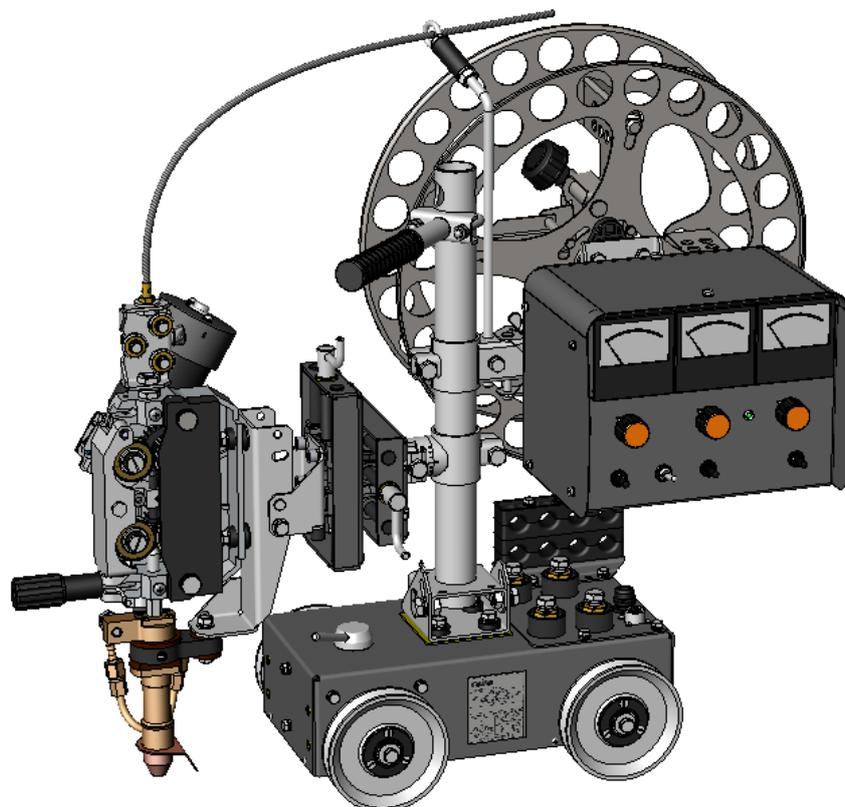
Автомат сварочный АДГ-630 исп.-01 (с БУ-23).
